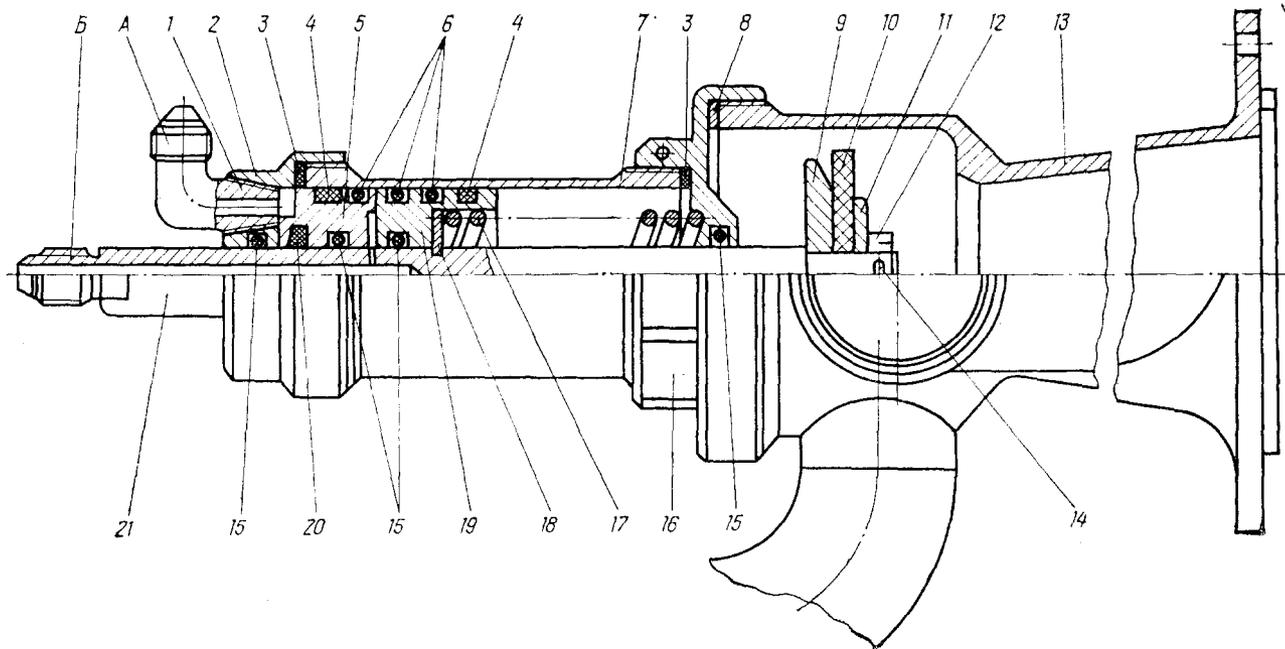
в (ТК № 29). Пневмоклапан 2102.0272.160 в сборе с корпусом 2102.0272.170 (вып. 7):
